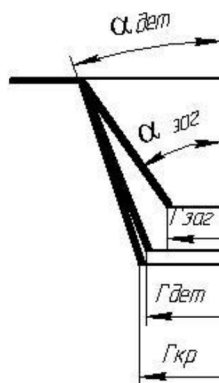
Схема определения пружинения в процессе отбортовки
